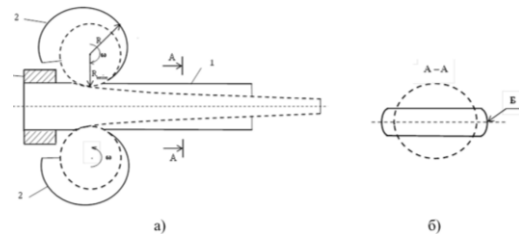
Схематичне зображення процесу вальцювання на клин а); переріз деформованої заготовки; б) Б – поверхня контролю за деформаціями і руйнуванням
